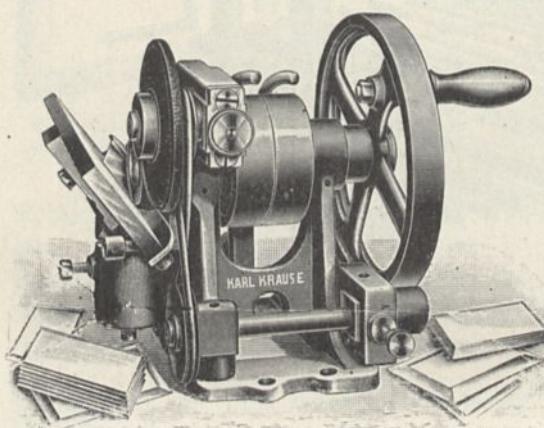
Kantenabschrägmaschine mit Kreismesser.
